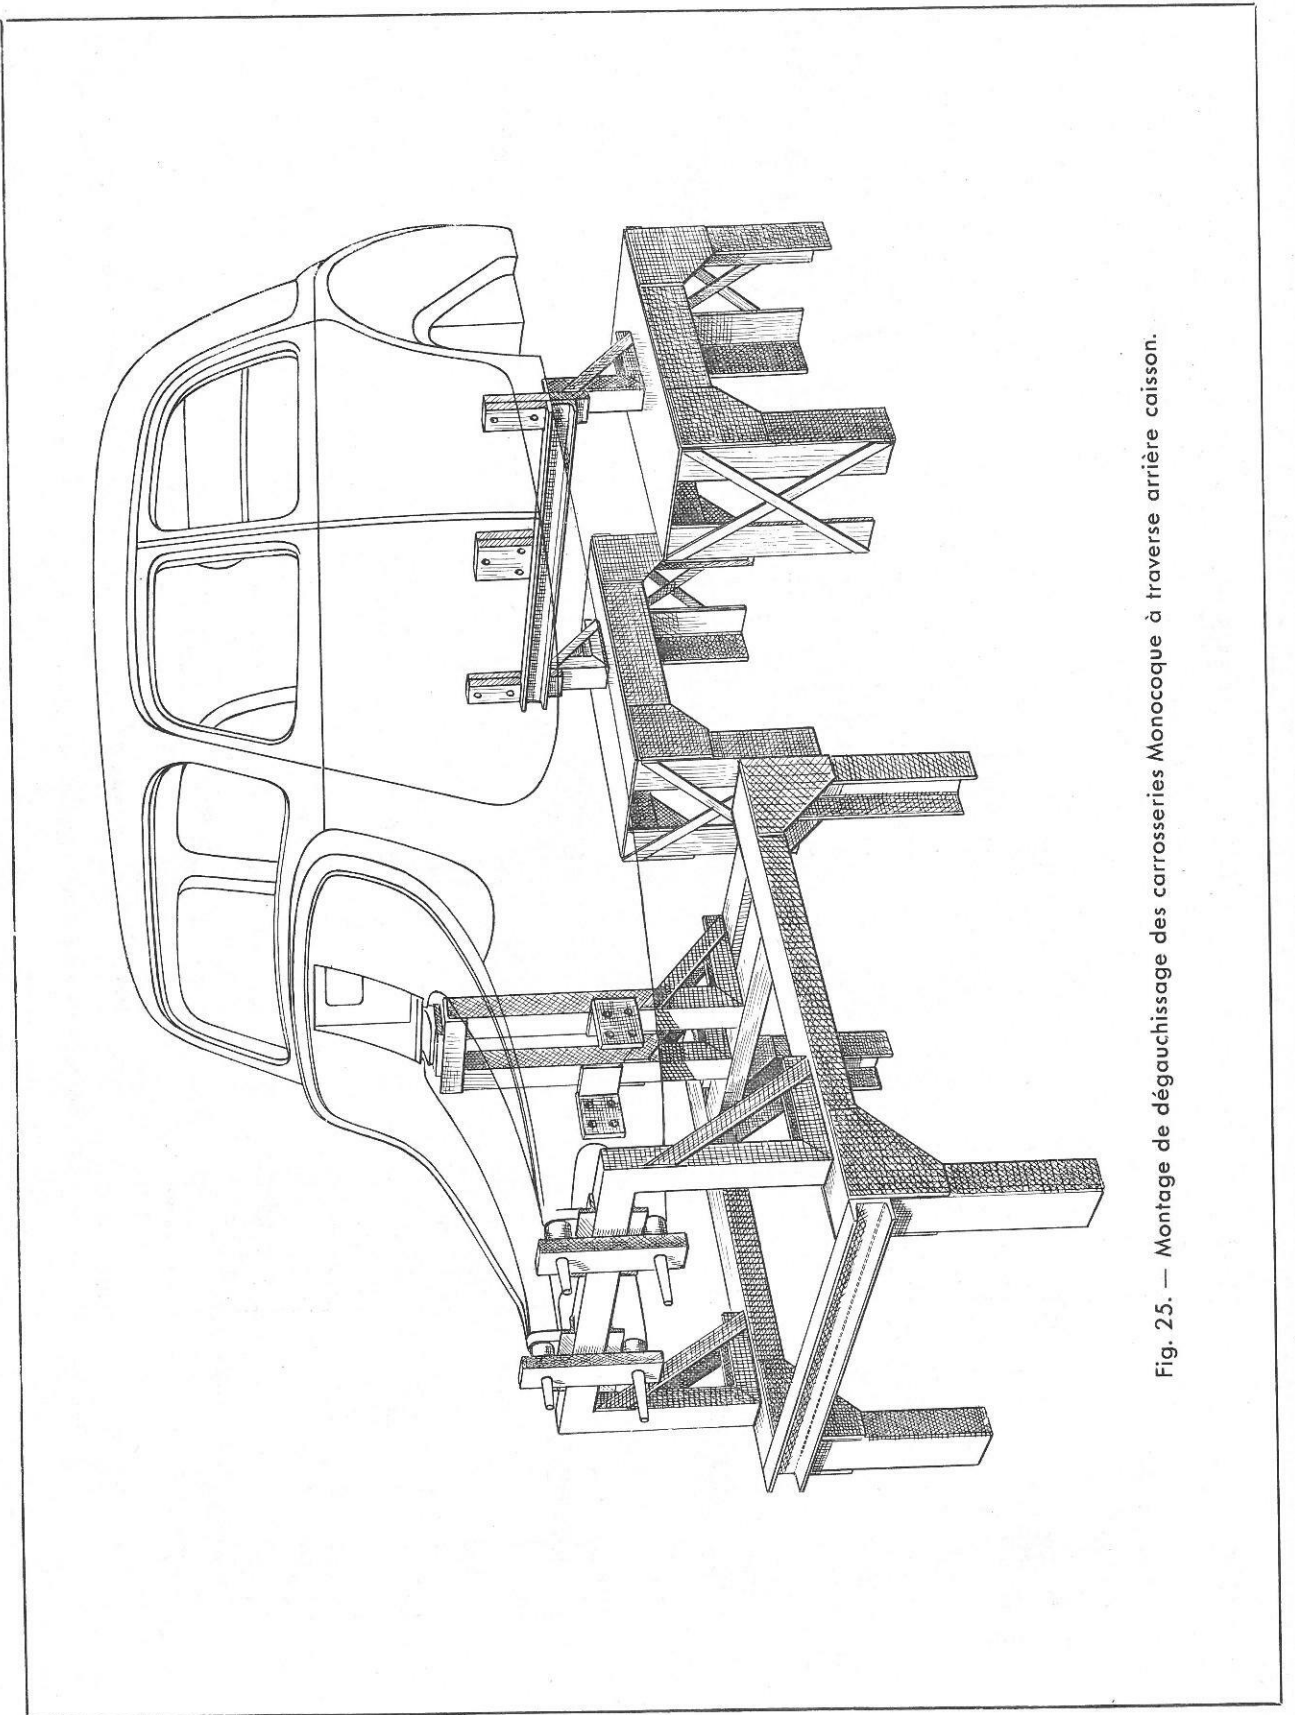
Montage de dégauchissage des carrosseries Mono-coque à traverse arrière caisson.
